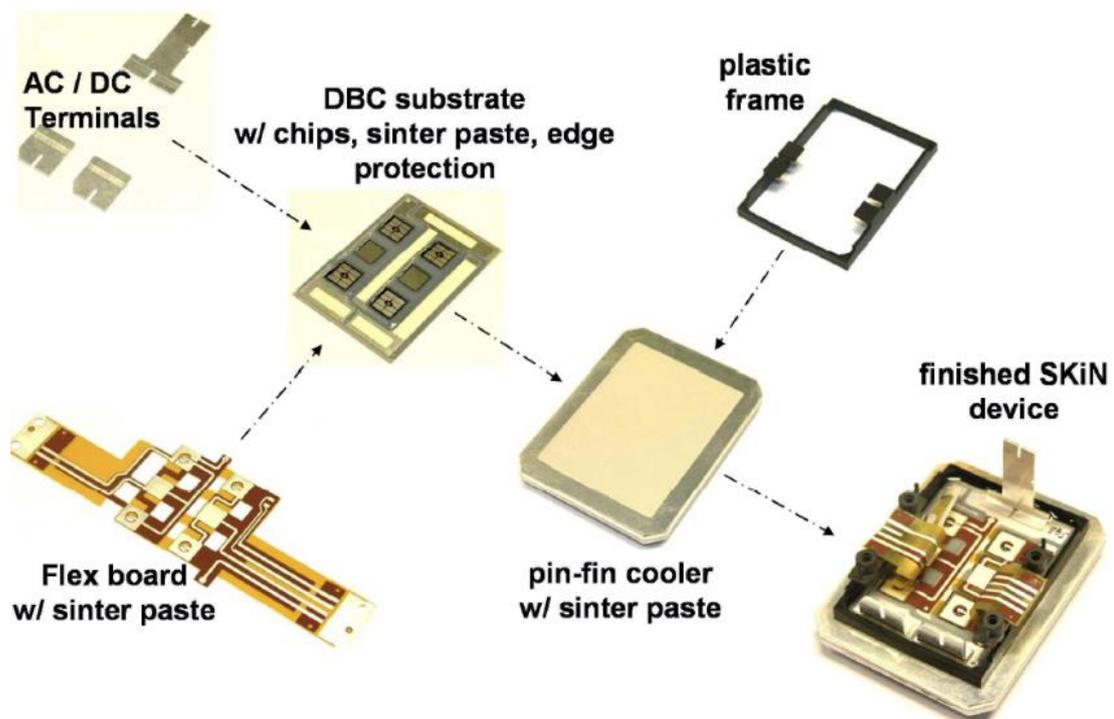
Explosionsansicht eines SKiN Moduls. Quelle: [51]
